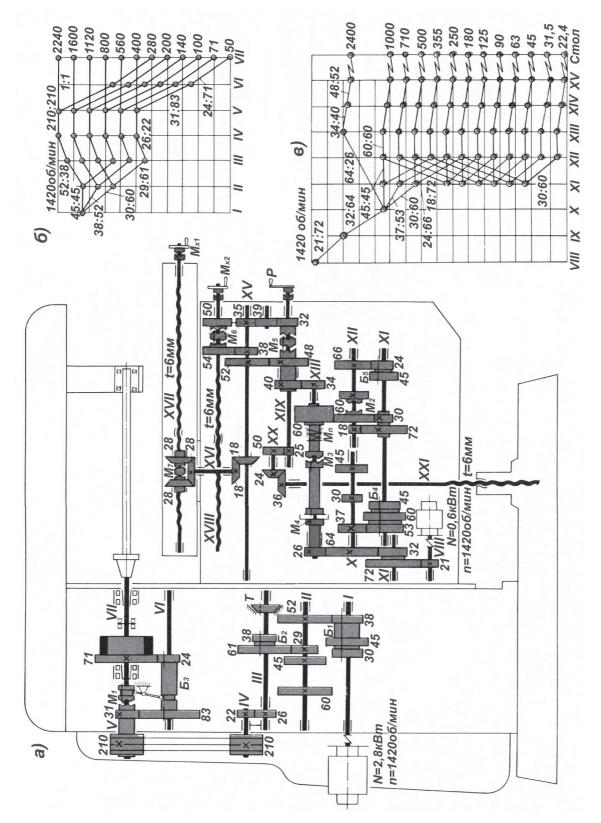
Кинематическая схема горизонтально-фрезерного станка модели 6П80Г
